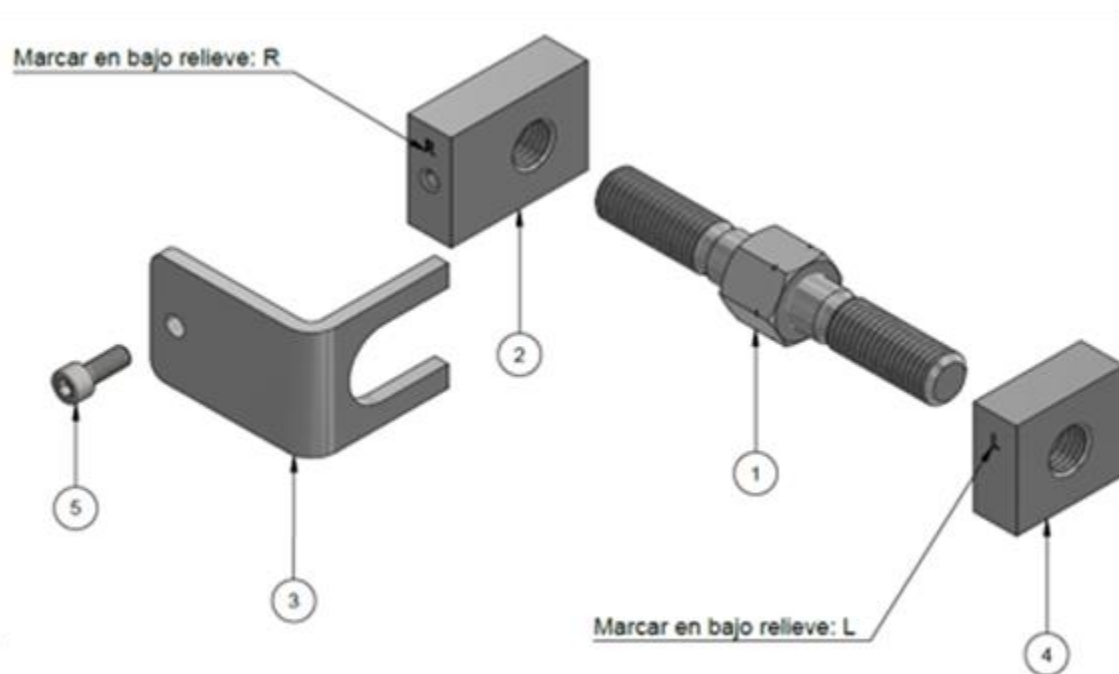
Vista explosionada del kit de tornillos M16, (1) tornillo especial M16, (2) tuerca derecha, (3) platina guía, (4) tuerca izquierda y (5) tornillo Allen [3].
